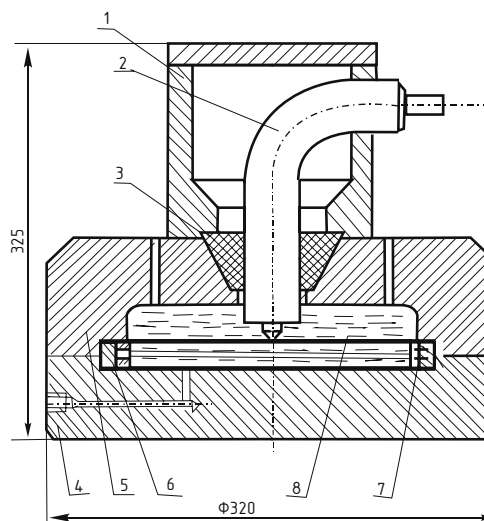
Приспособление для раздачи колец ГМП: 1 – стакан; 2 – электрод; 3 – гайка; 4 – камера; 5 – крышка; 6 – обойма; 7 – обрабатываемая деталь; 8 – камера.
